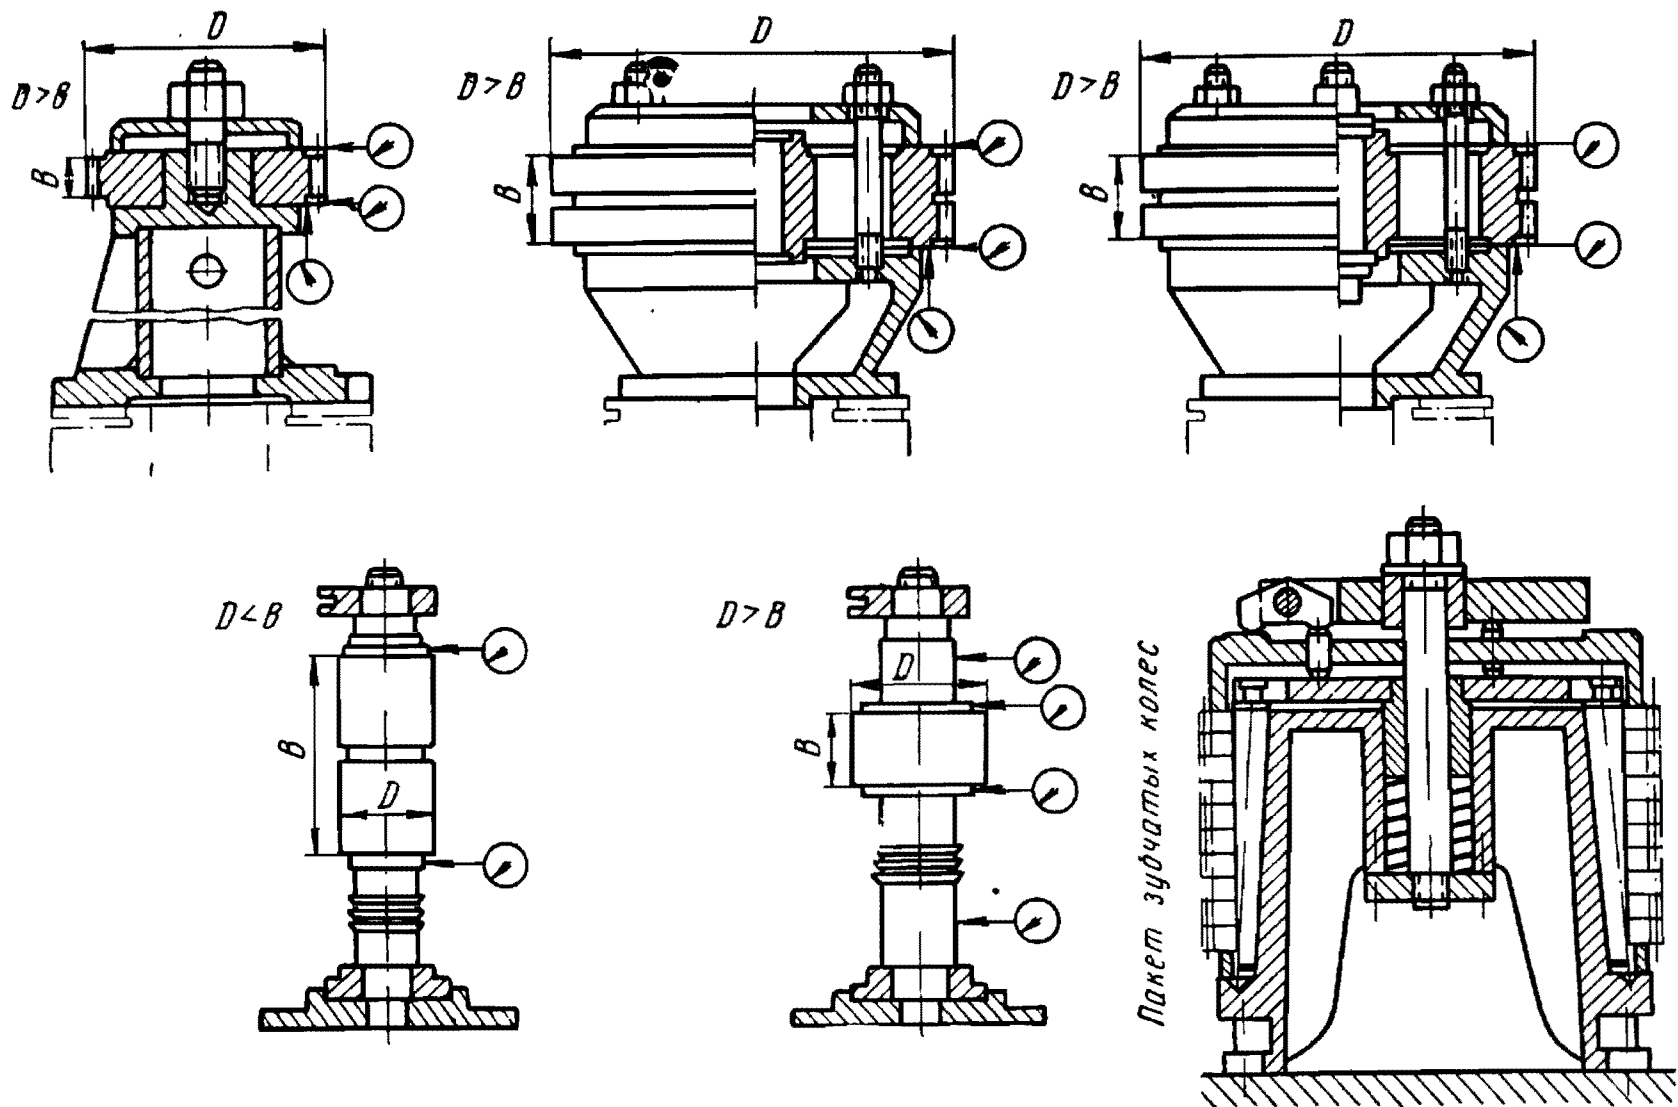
Схемы установки, крепления и выверки заготовок колес на зубофрезерных станках
